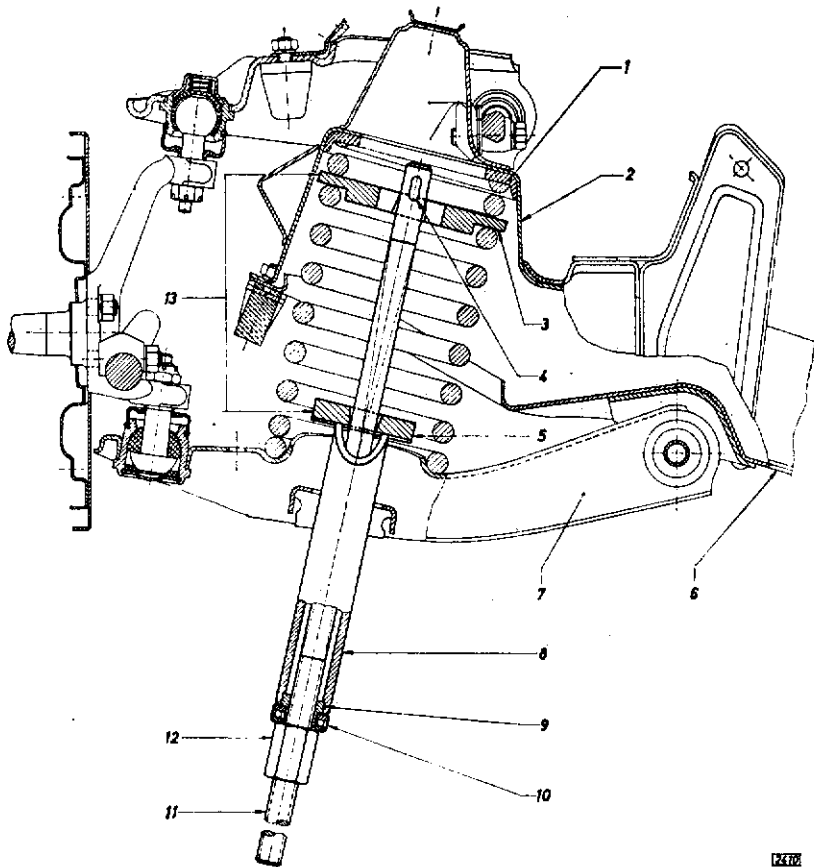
Compresseur de ressort en place — outils S-1034 et S-1158
